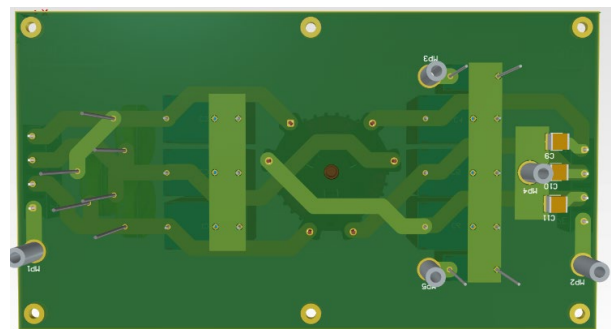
3D Bottom Ansicht 3-Phasen-Filter-PCB.
